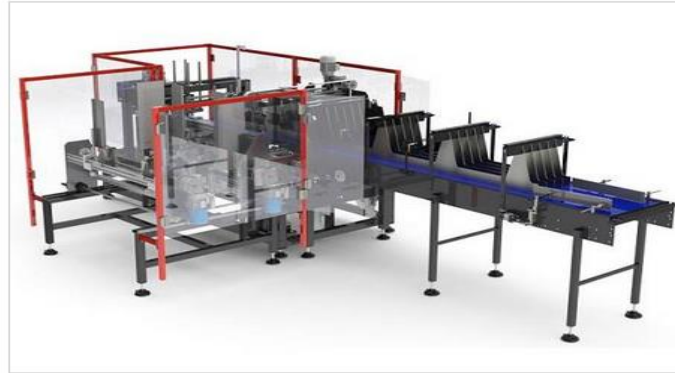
Máquina encajadora automática “Wrap around”- EarFlap War150
